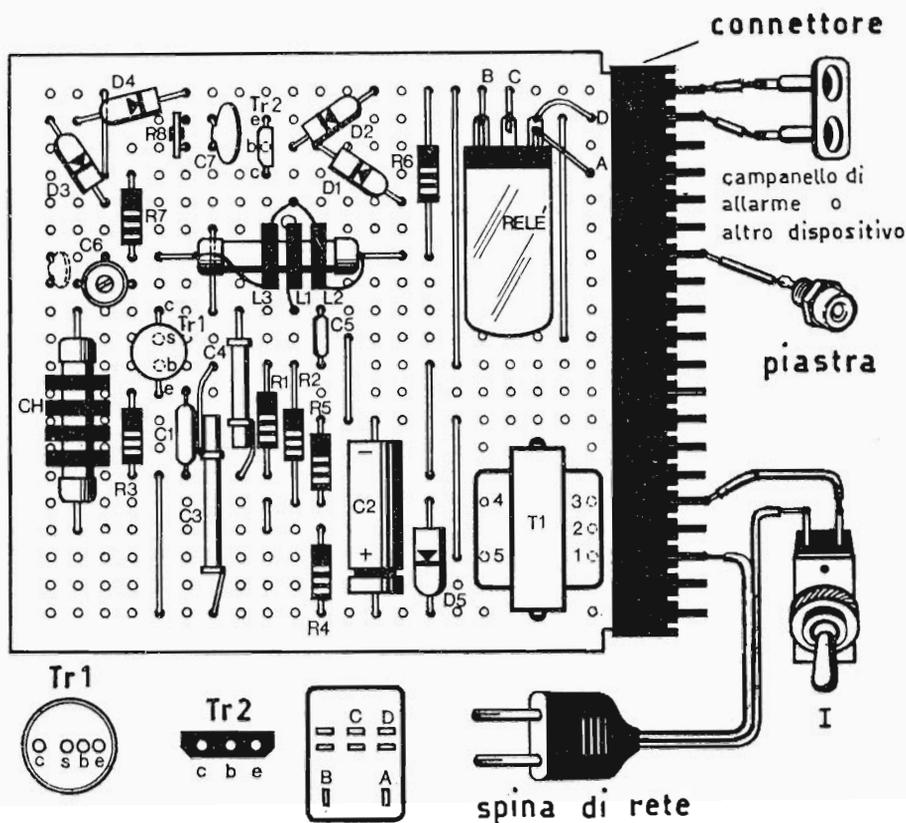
Schema pratico di montaggio del Sensor-Matic.
